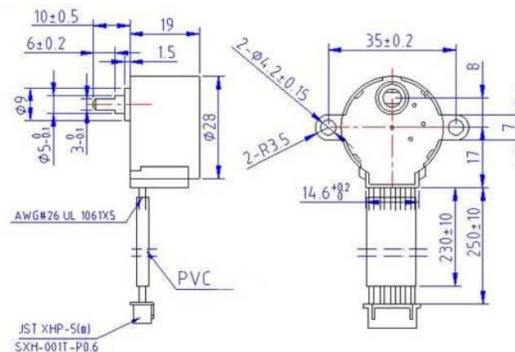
Габаритні розміри крокового двигуна 28BYJ-48
